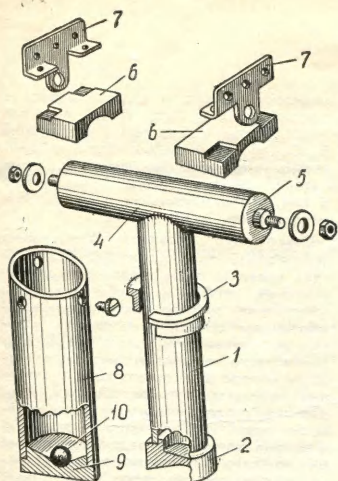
Опорный шарнир: 1—стойка; 2—наконечник; 3—кольцо; 4—осевая трубка; 5—наконечник; 6—подшипники; 7—ушки; 8—стакан; 9—пробка; 10—шарик.
